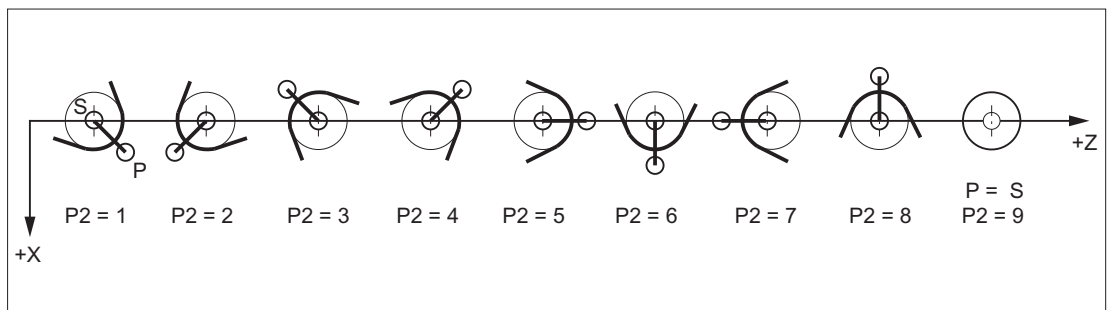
刀具参数 2 (P2)：在车削中心前侧加工时
